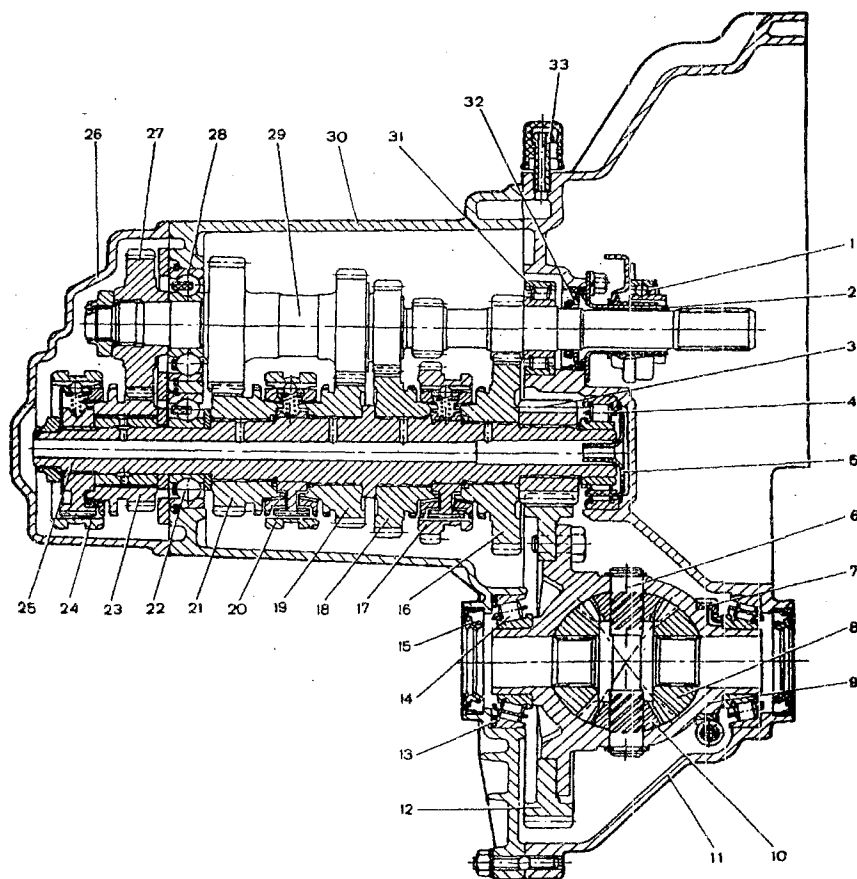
Чертеж коробки передач автомобиля ВАЗ-2110:
